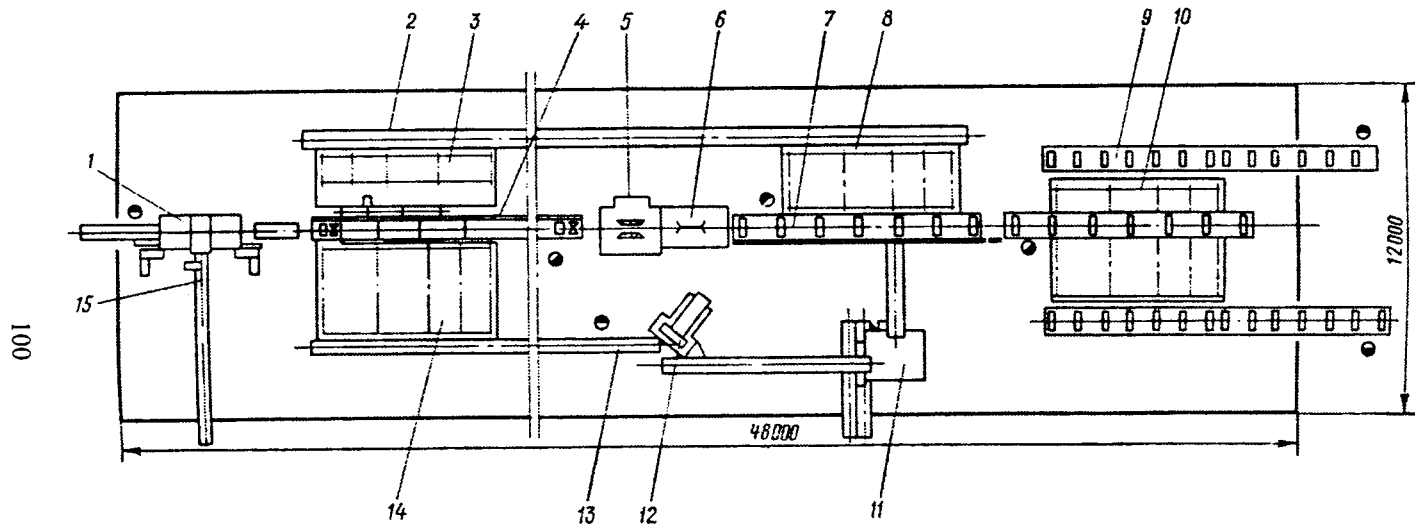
Схема лесопильного цеха с головным фрезерно-брусующим станком для переработки тонкомерного сырья (ЦНИНМОД):
